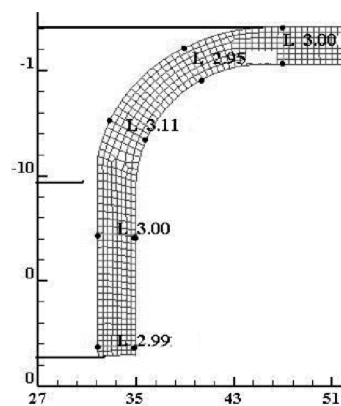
Кінцеві розміри (L) в міліметрах відборткованої частини заготовки
